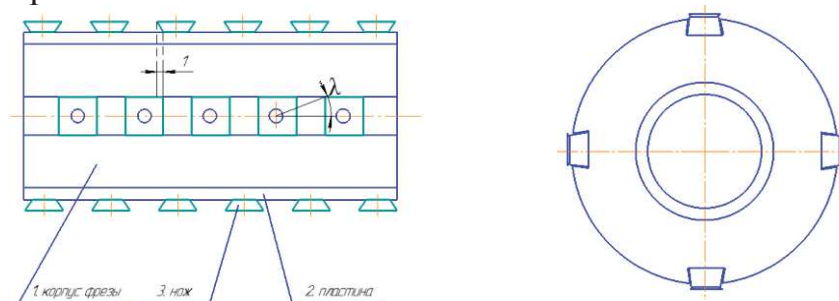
Фреза сборная с быстро заменяемыми ножами
